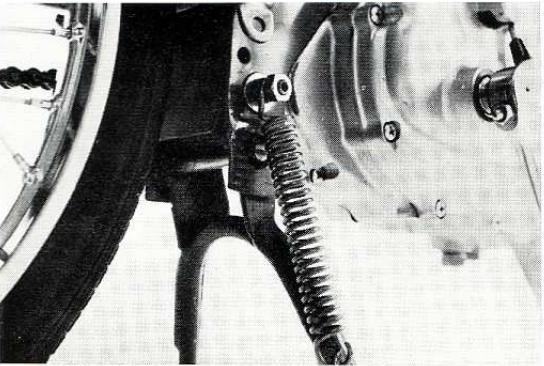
DEMONTAGE DE LA BEQUILLE.
